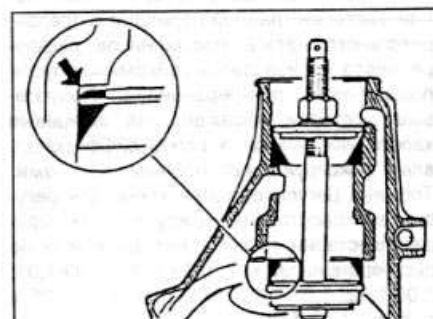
Установка наружного кольца внутреннего подшипника ведущей шестерни с дистанционным кольцом (показано стрелкой) при помощи приспособления 15.083
